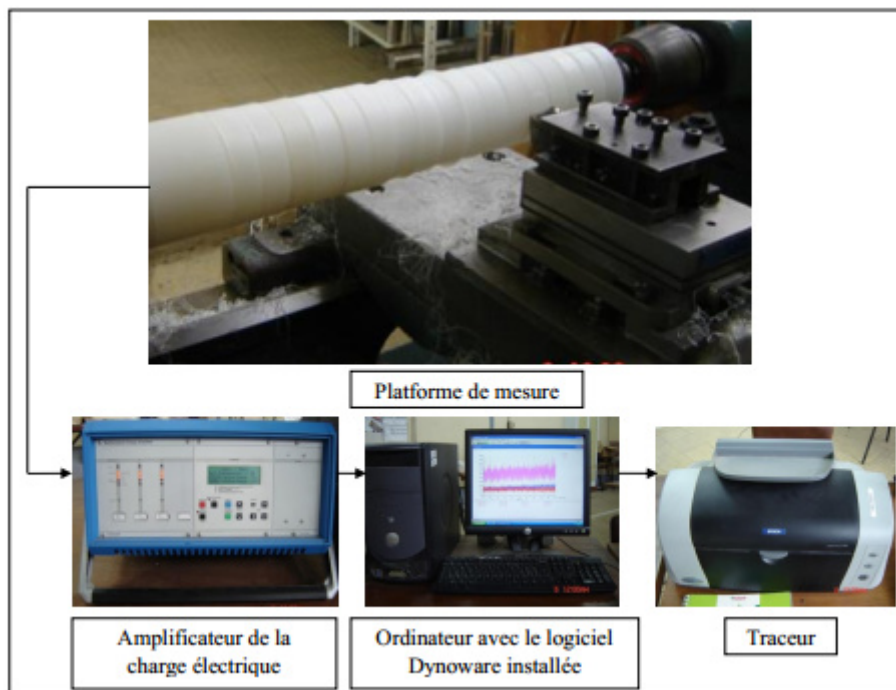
Montage de la chaîne et plateforme de mesure des efforts de coupe.
